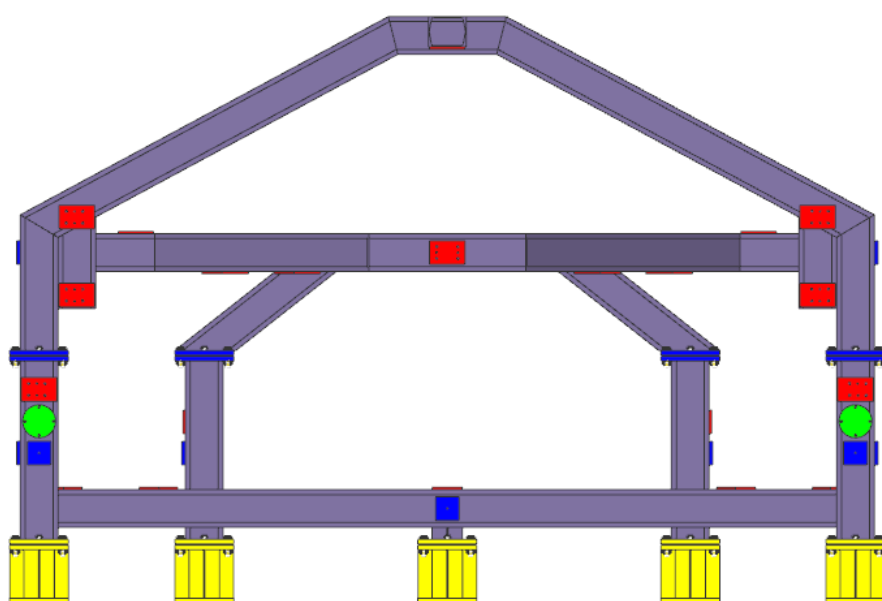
Общий вид каркаса сборного приспособления (вид сзади).
